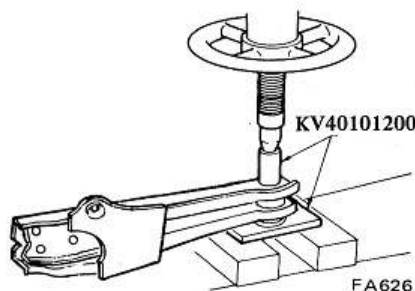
Dépose de la bague élastique du bras de suspension
